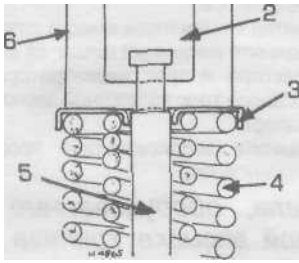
Самодельное приспособление для снятия и установки сухарей на стержни клапанов
